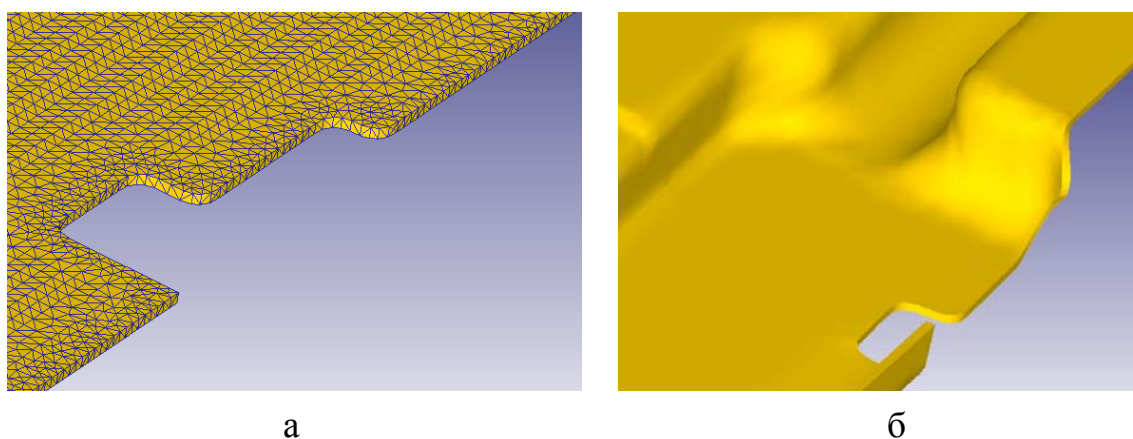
Моделювання деформування заготовки з початковою геометрією:
